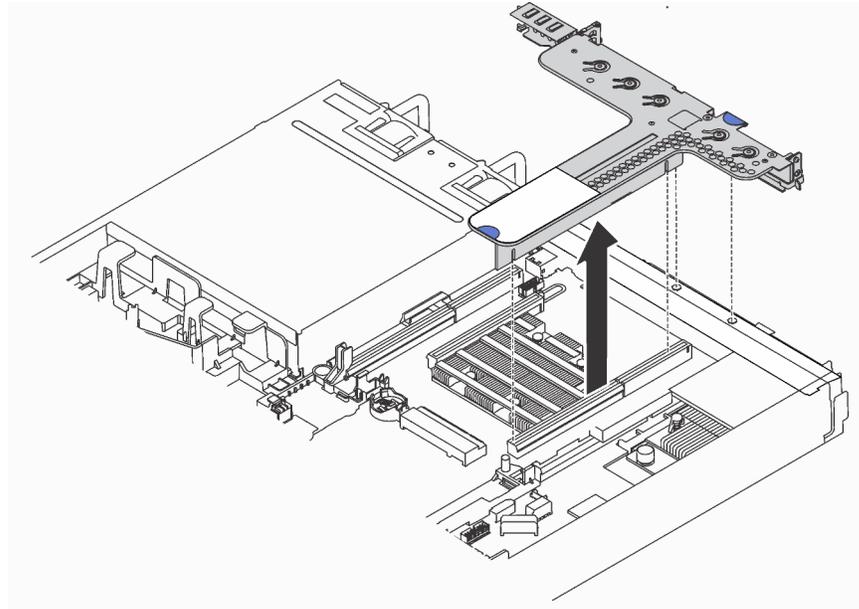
Entfernen der Adapterkartenbaugruppe
